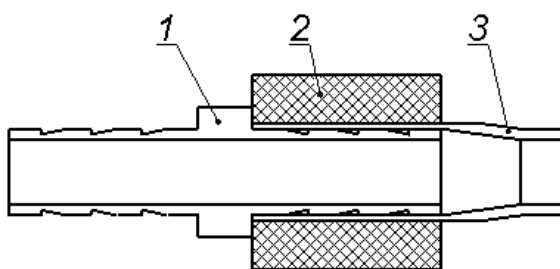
Крепление ПМ: 1 – штуцер; 2 – крепежная часть каркаса; 3 - ПМ
